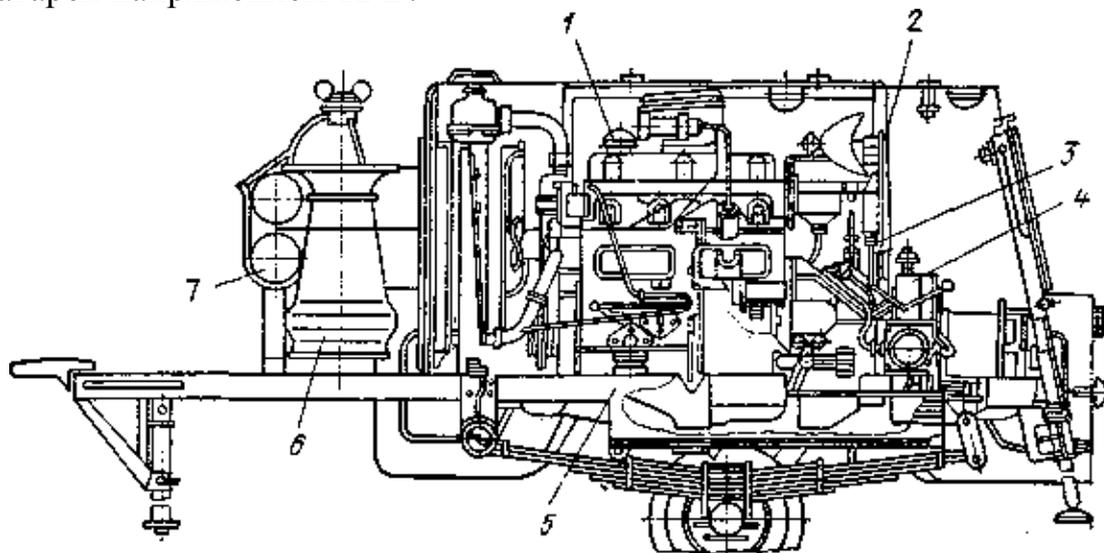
Мотопомпа МП–1600: 1 – двигатель; 2 – пульт управления; 3 – вакуумный кран; 4 – центробежный насос; 5 – рама; 6 – генератор пены ГПС–600; 7 – всасывающий рукав
